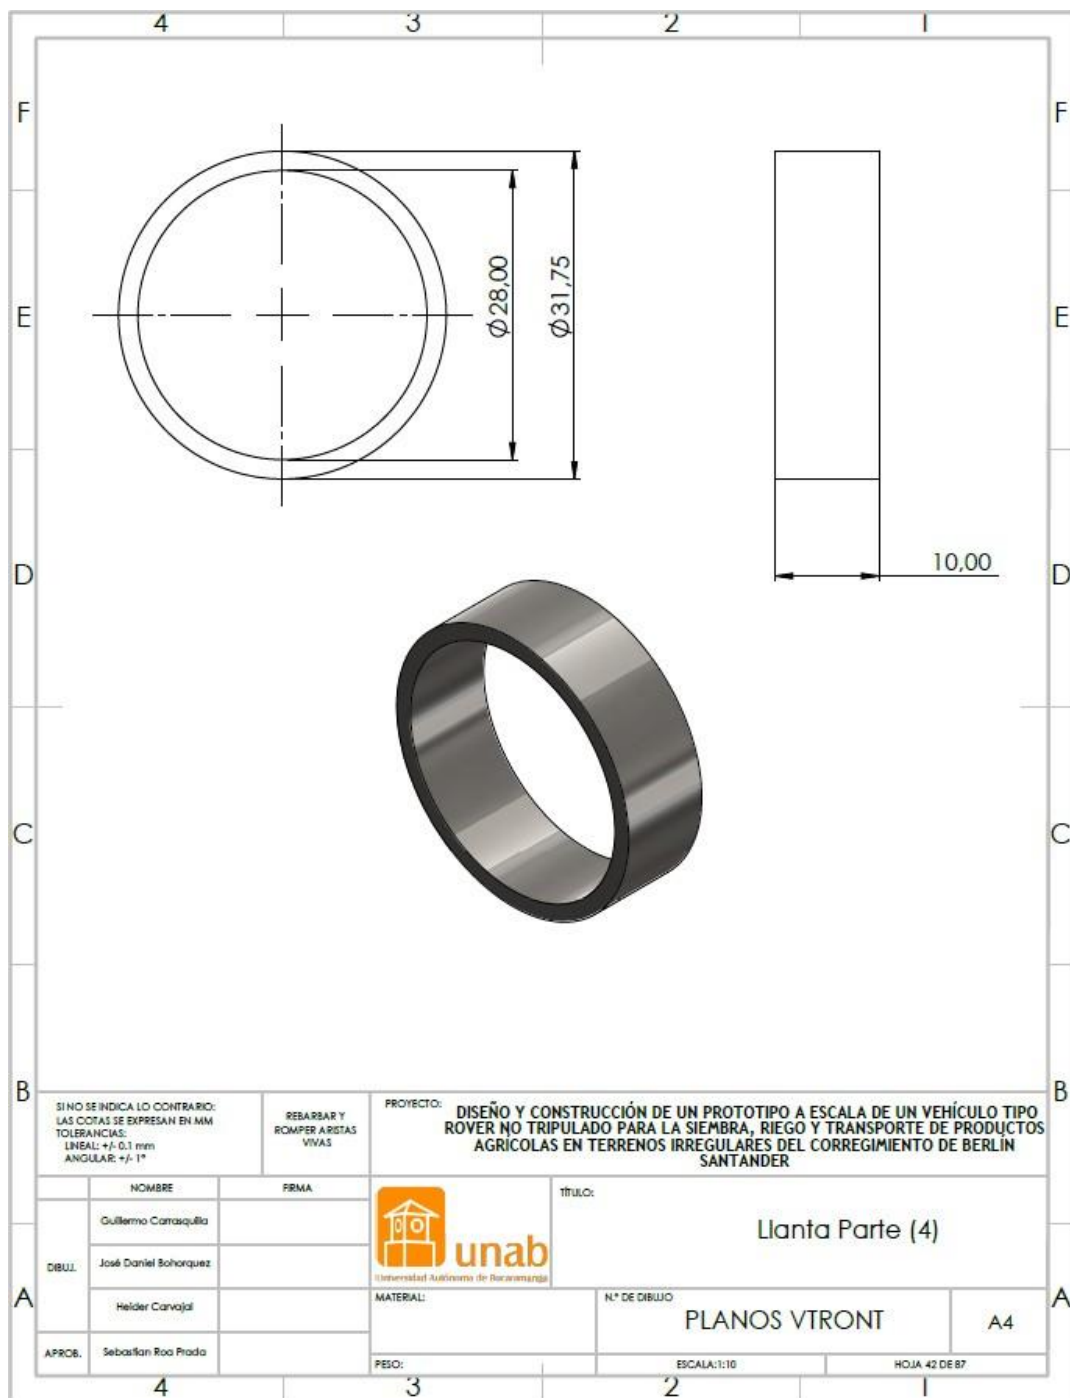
Plano de cote de tubería para la llanta parte 4.
